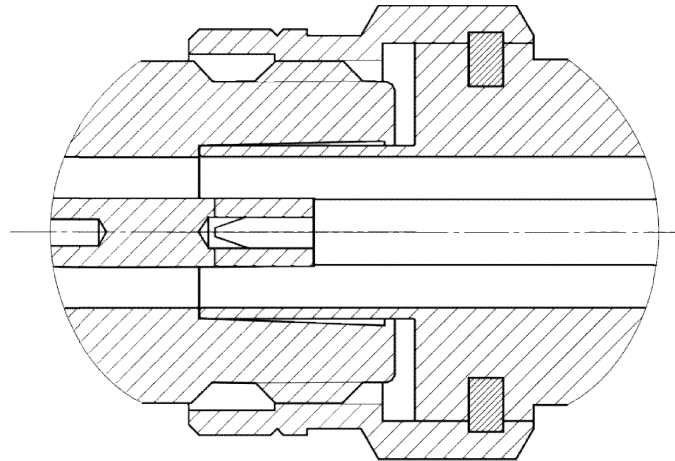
Соединители тип N и III (розетка слева, вилка справа)
